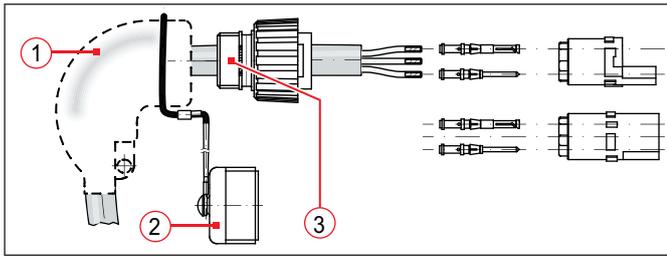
Beispiel für Stecker mit Gewinde und 90° Form-schrumpfteil (gilt analog auch für Dosen mit Gewinde)
